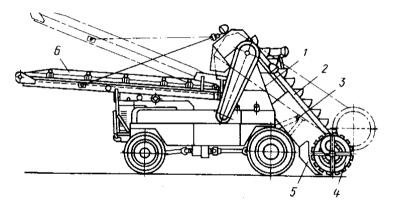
Многоковшовый погрузчик: 1 – самоходное шасси; 2 – ковшовый элеватор; 3 – гидроцилиндры; 4 – подгребающий шнек-питатель; 5 – отвал; 6 – поворотный ленточный конвейер
